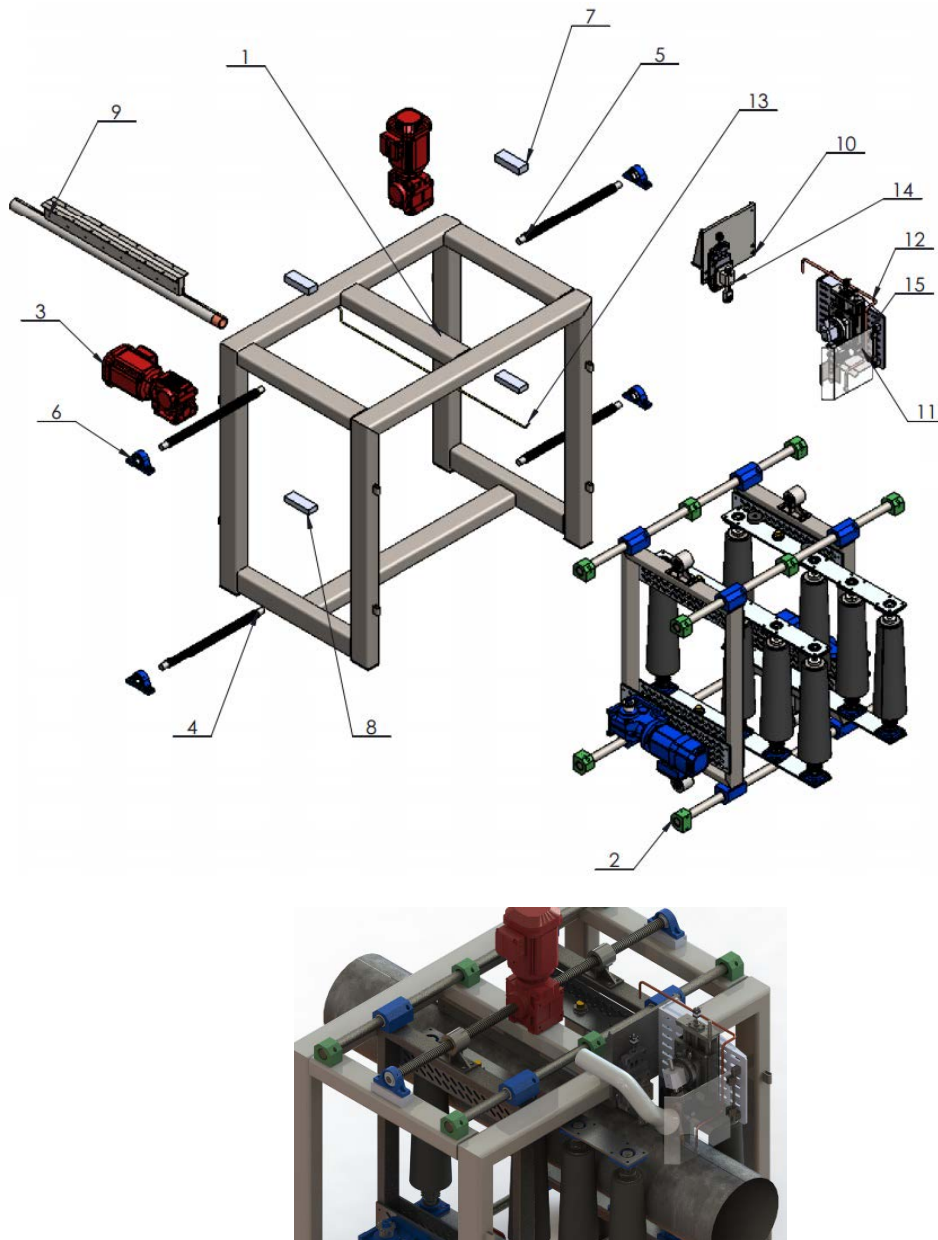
Equipamento de soldadura, representado em vista isométrica explodida e assemblada
